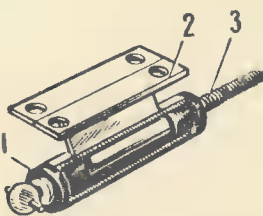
Детали рулевого устройства — водяного охлаждения двигателя:
